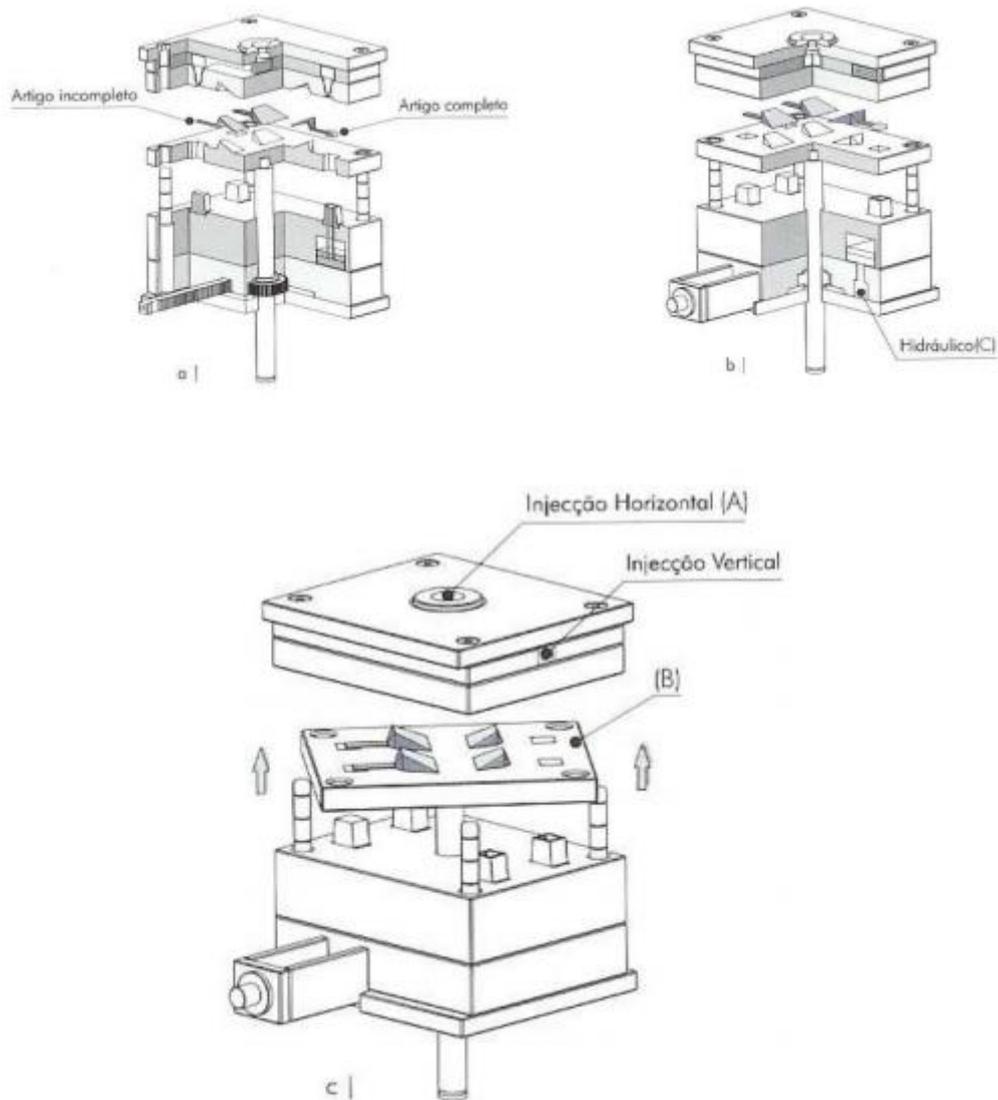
Molde bi-material a) Abertura do molde; b) Abertura do molde e corte; c) Abertura Molde (Cunha, et al., 2003)
